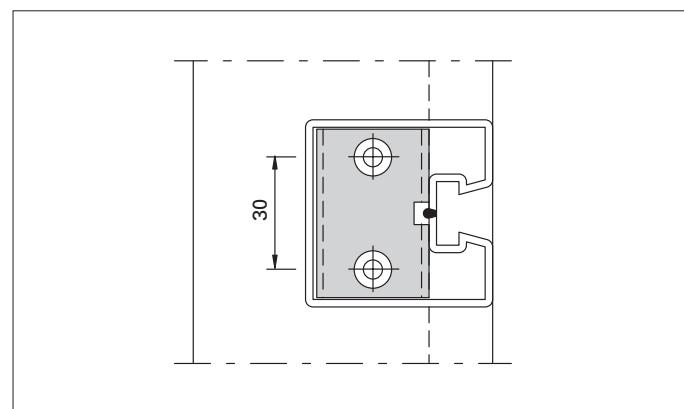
T-Verbinder mit Freistellung im Schweißnaht-Bereich
